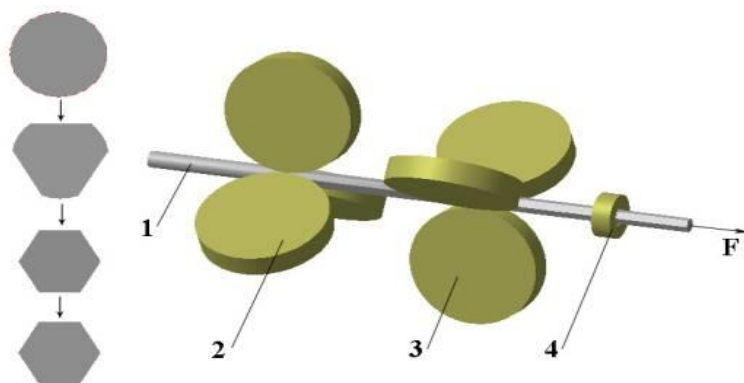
Схема трёхступенчатого деформирования за один проход: 1 – заготовка; 2 – трехроликовый калибр первой ступени деформации; 3 - трехроликовый калибр второй ступени деформации; 4 – монолитная волока
